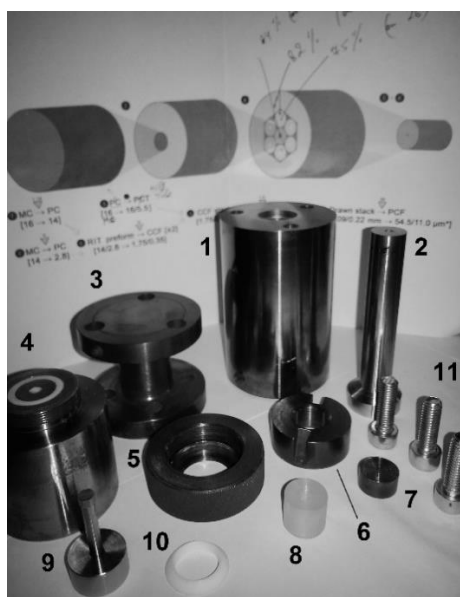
Детали оснастки для третьего этапа экструзии: 1 – контейнер; 2 – давящий плунжер; 3 – переходный элемент между контейнером и прессом; 4 – основание плунжера; 5 – накидная гайка на плунжер; 6 – направляющая для плунжера; 7 – заглушка; 8 – заготовка с продольным отверстием  $\text{AgCl}_{0,18}\text{Br}_{0,82}$ ; 9 – разборный гексагональный дорн (плунжер); 10 – уплотнительное кольцо; 11 – болты для соединения контейнера и переходного элемента
